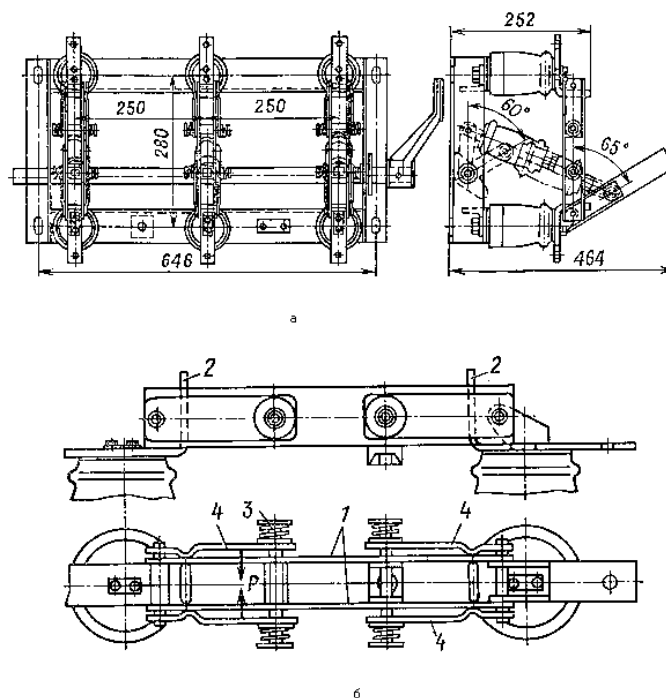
Триполюсний роз'єднувач внутрішньої установки типу РВ-10/1000
